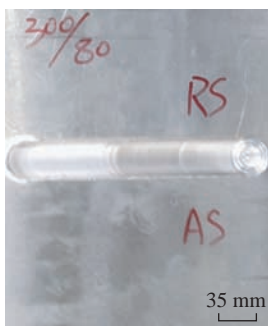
AZ31镁合金双面搅拌摩擦焊接接头表面形貌
